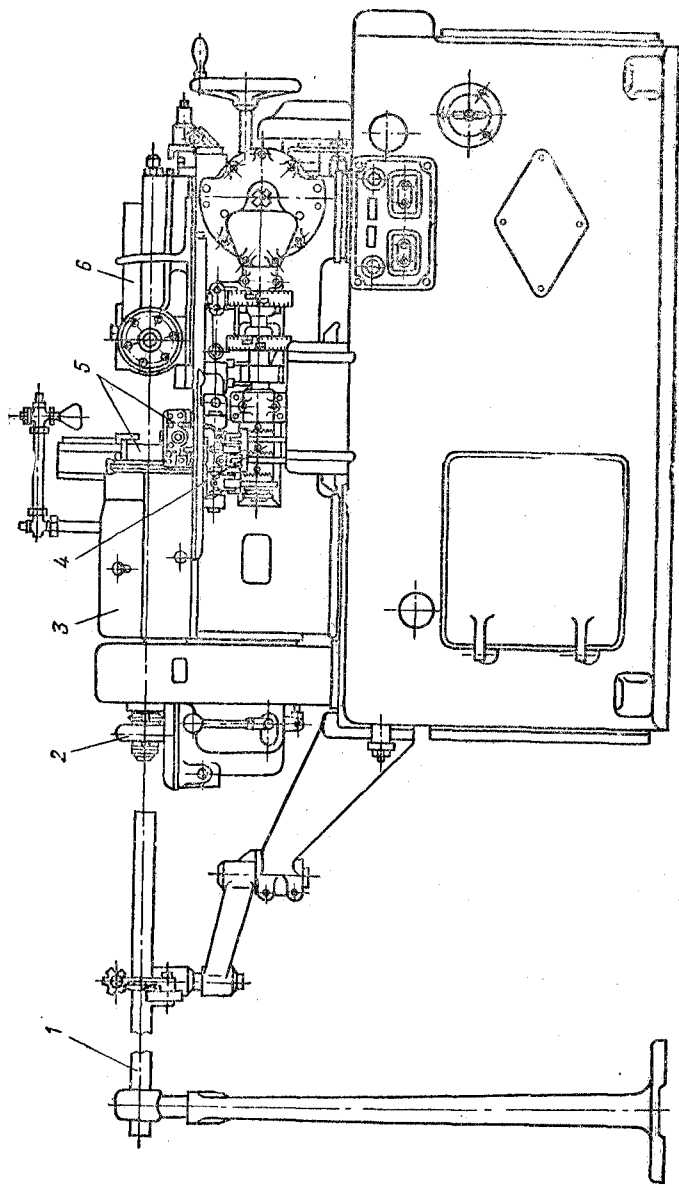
Одношпиндельный токарно-револьверный автомат модели 1A136
